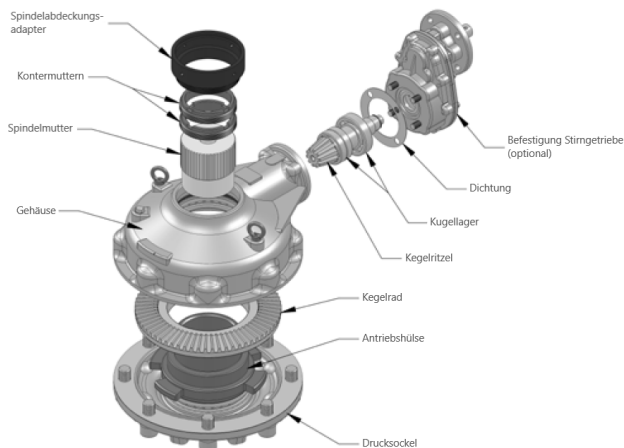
Explosionsansicht eines Standard SB V Getriebe
